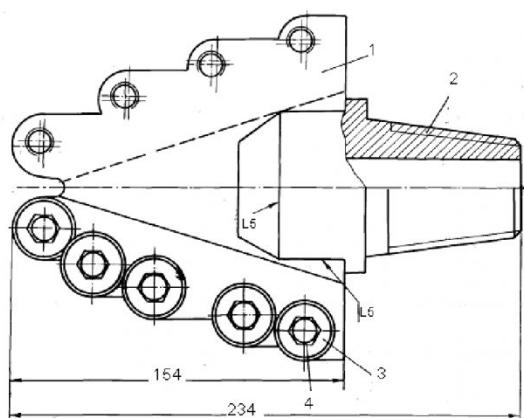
Буровое долото с механическим креплением к корпусу пластин твердого сплава
